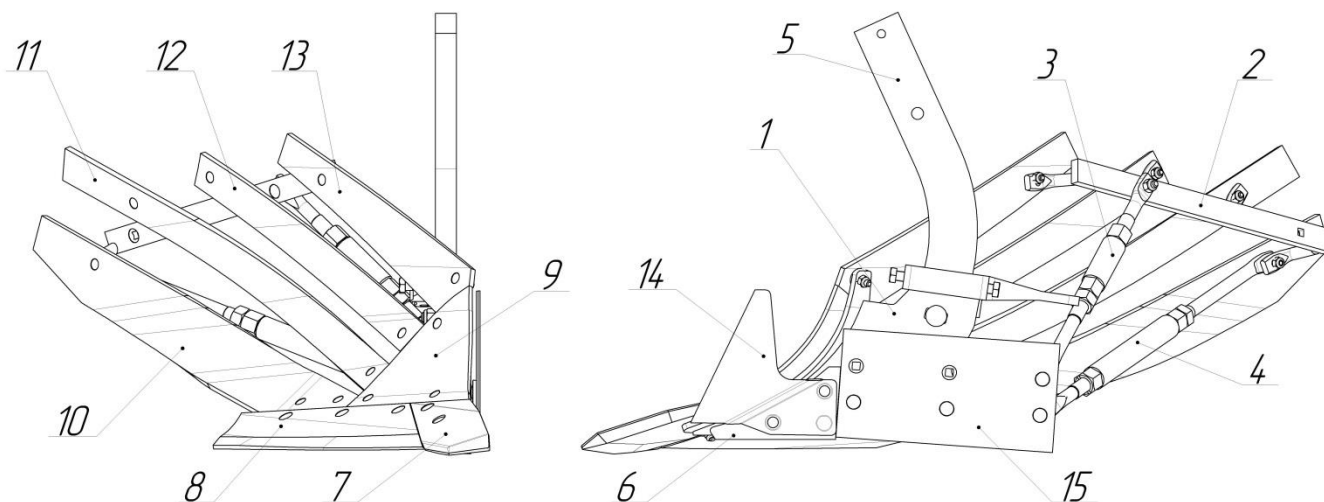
Корпус ПО-40.000-01 (правооборачивающий)
